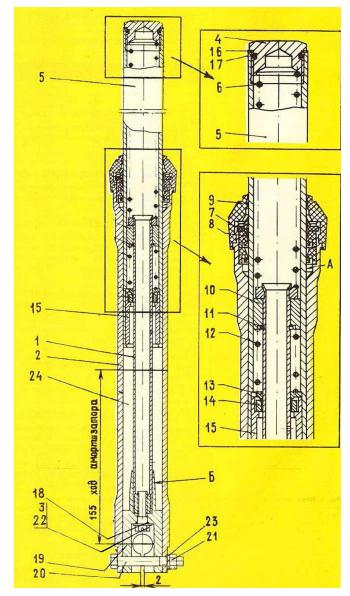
La barra de la horquilla: 1-tubo interior; 2-tubo móvil; 3-tornillo; 4-tapón; 5-tubo fijo; 6-resorte de suspensión; 7-reten; 8-puño; 9-capuchón; 10-émbolo; 11-anillo especial; 12-resorte de retroceso; 13-anillo; 14-válvula del amortiguador; 15-cuerpo de la válvula; 16-arandela; 17 junta en anillo; 18-anillo de goma; 19-extremo inferior; 20-bulón M8; 21-tuerca M8; 22-arandela; 23-arandela; 24-recipiente del aceite.
